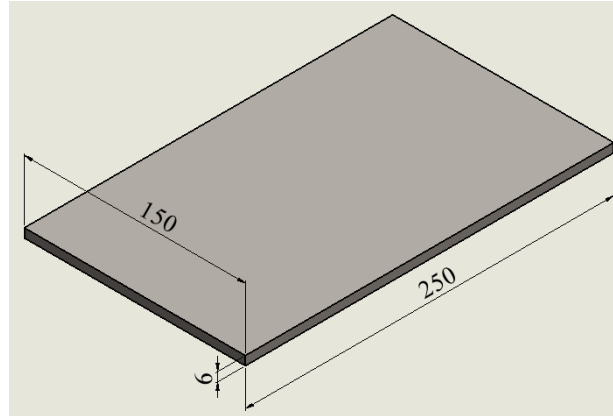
Dimensiones de la placa de acero ASTM A – 36.
